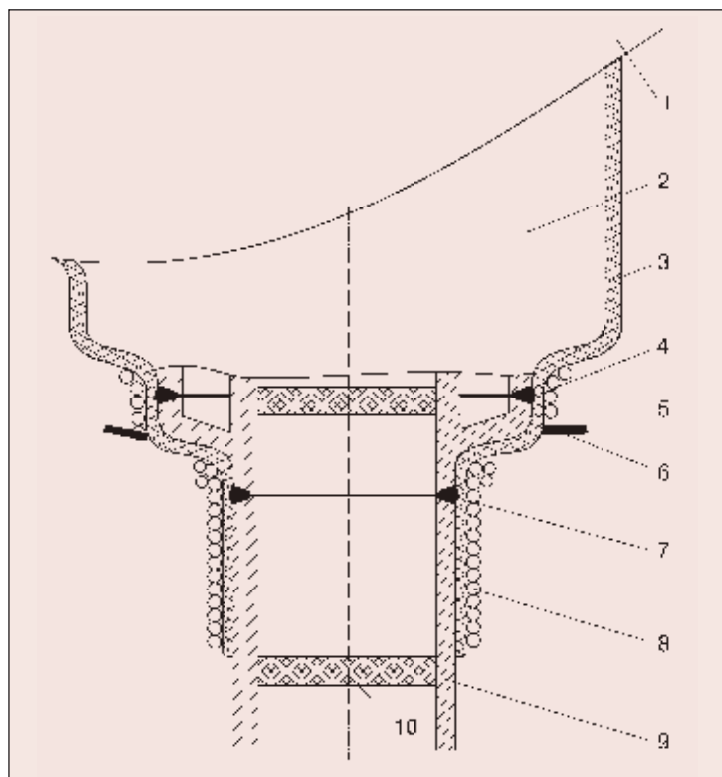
Схема установки индукторов при местной термической обработке сварных соединений труб с коллектором парогенератора на АЭС с реактором ВВЭР-1000: 1 — корпус парогенератора; 2 — коллектор; 3 — теплоизоляция; 4 — сварной шов коллектора; 5 — индуктор, установленный на коллекторе (6–8 витков); 6 — ограничитель; 7 — сварное соединение трубы с коллектором; 8 — индуктор, установленный на сварном соединении трубы с коллектором (14–16 витков); 9 — труба; 10 — теплоизоляционная перегородка
